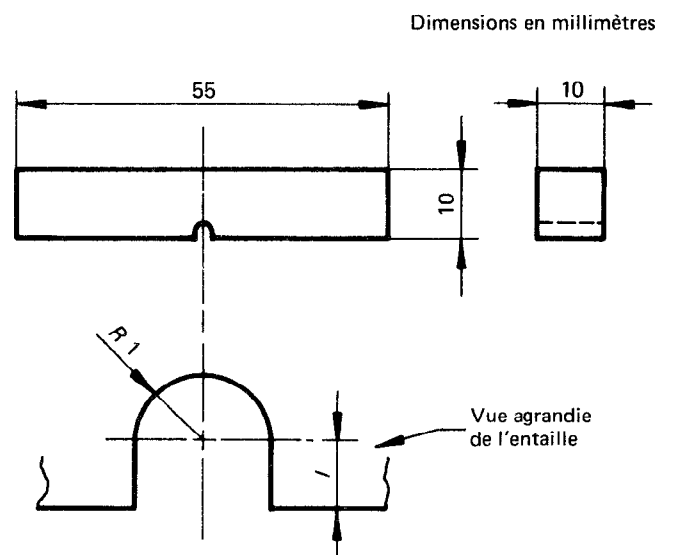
Dimensions de l'éprouvette Mesnager entaillée en U pour l'essai de choc
